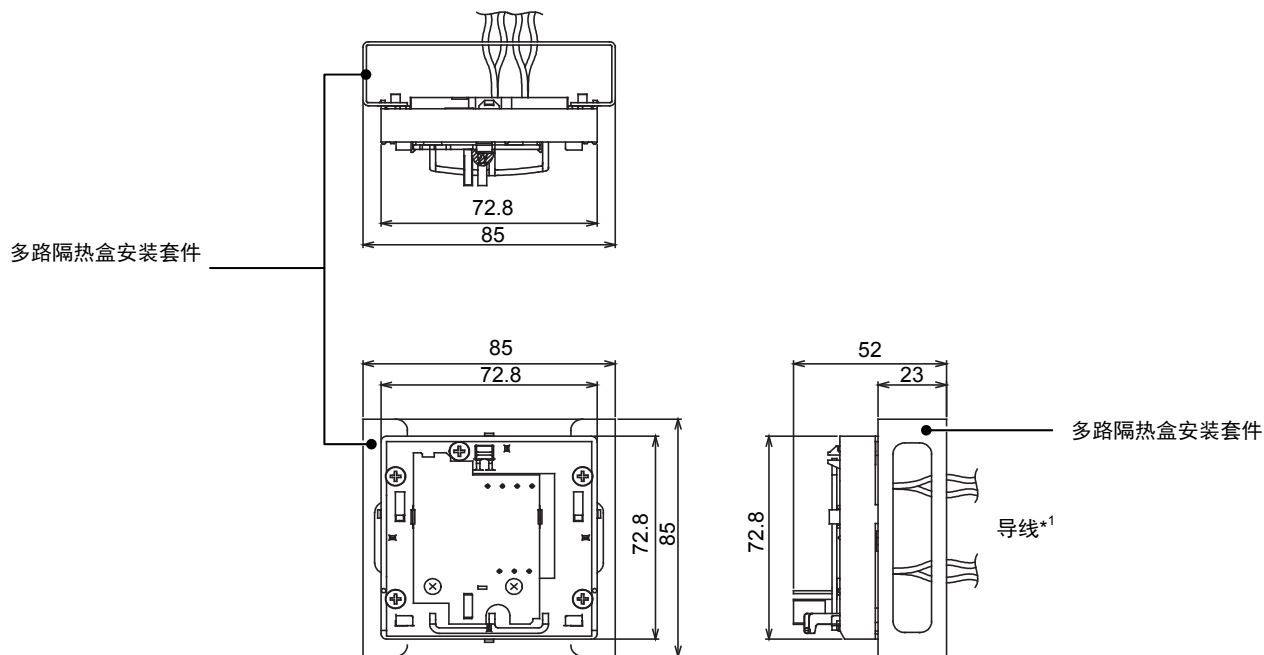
隔热板安装套件的安装表面尺寸图 (mm)
